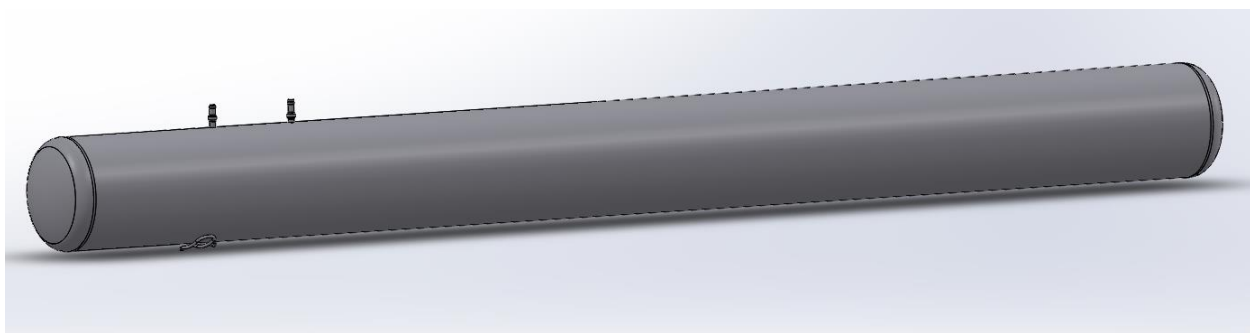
Трехмерная модель резервуара РЦГ-250
